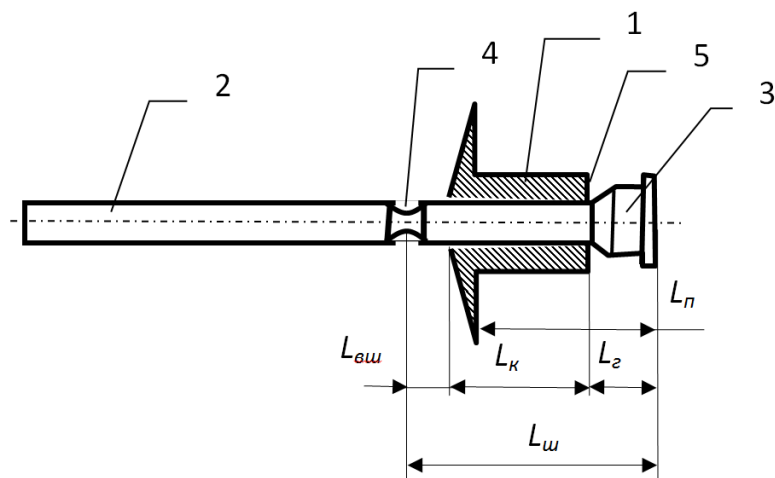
Конструкция шипа противоскольжения в форме стандартной вытяжной заклепки со ступенчатым сердечником с заданной точкой разрыва
